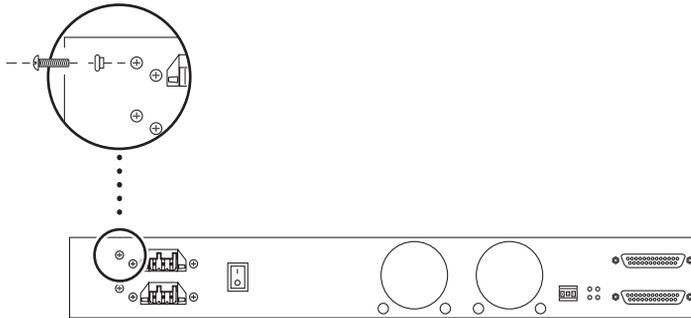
Fissaggio delle viti del collegamento a terra del telaio
